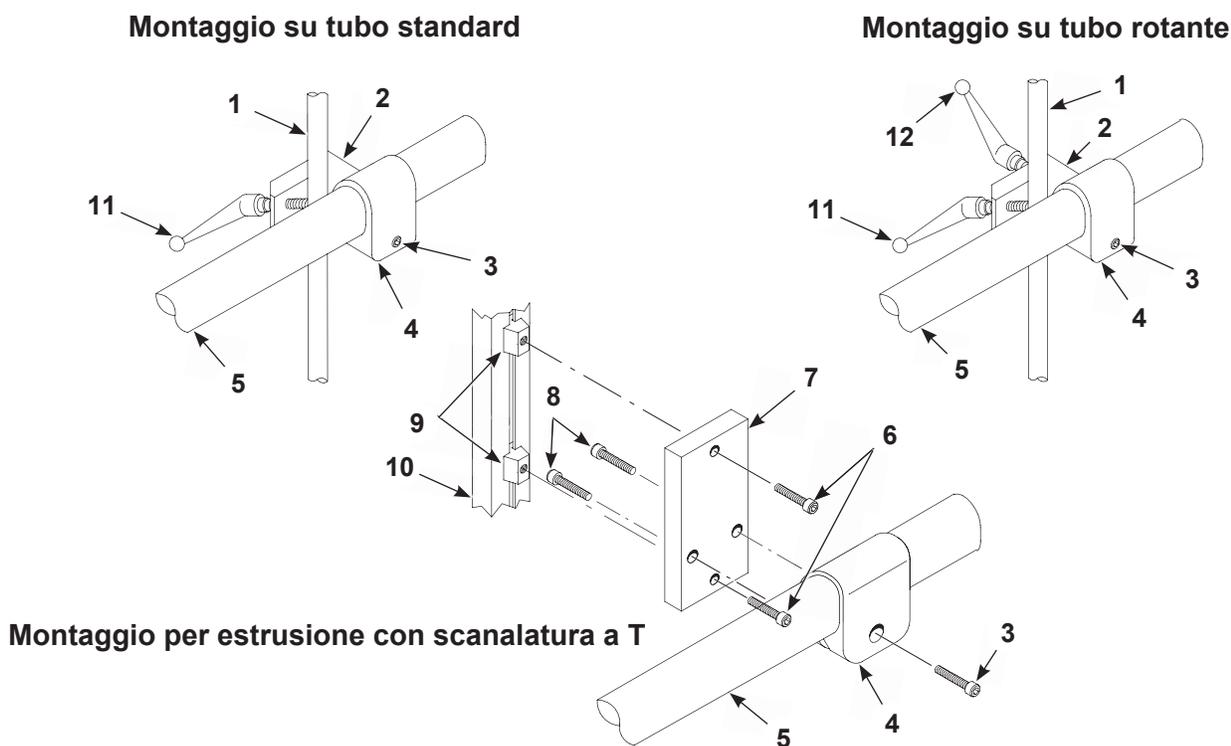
Kit di montaggio della pistola a spruzzo con montaggio su tubo
